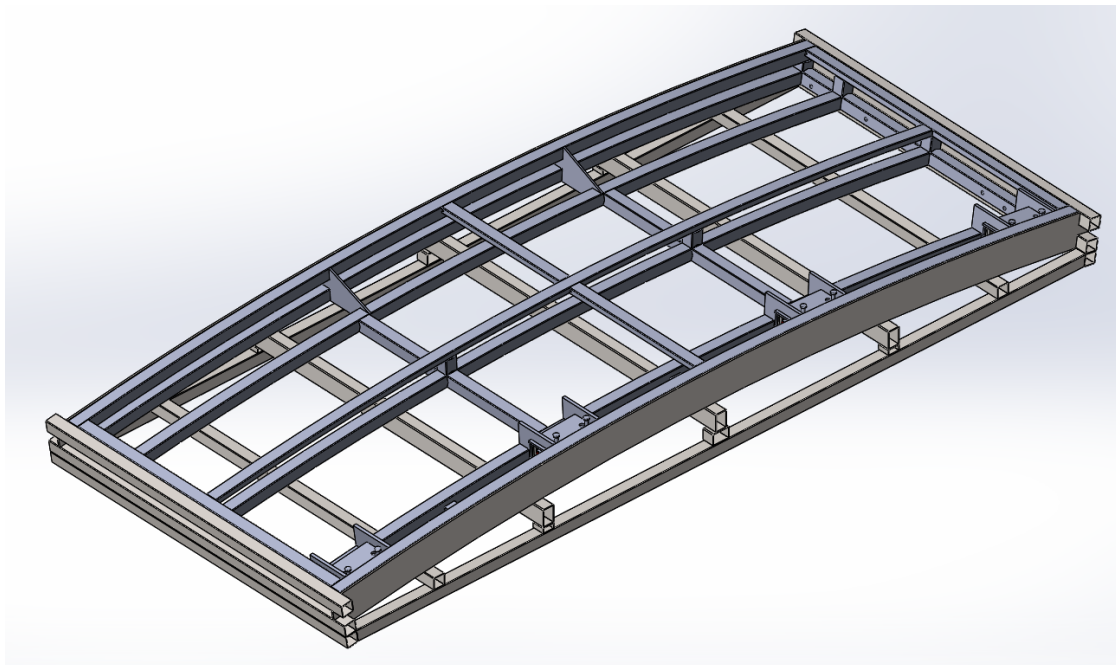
Макет кондуктора для сборки рам радиальных бортов
